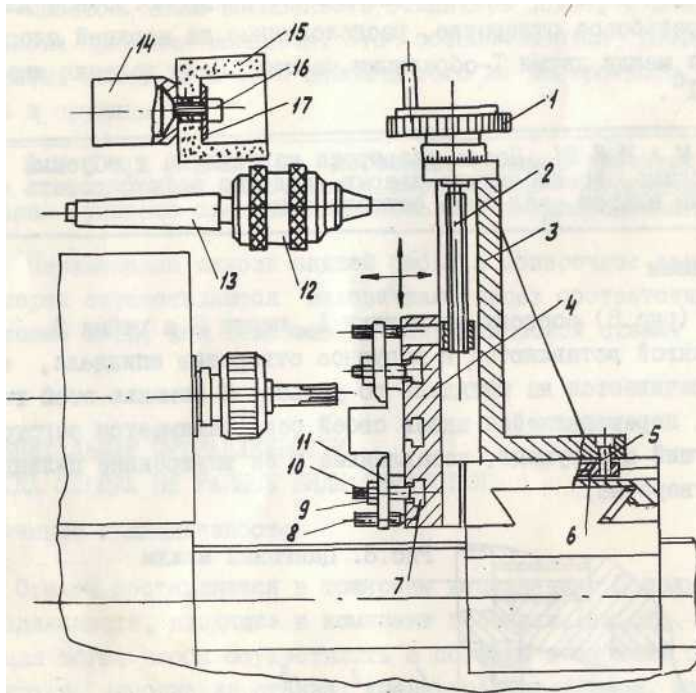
Фрезерно-сверлильное и плоскошлифовальное устройство
